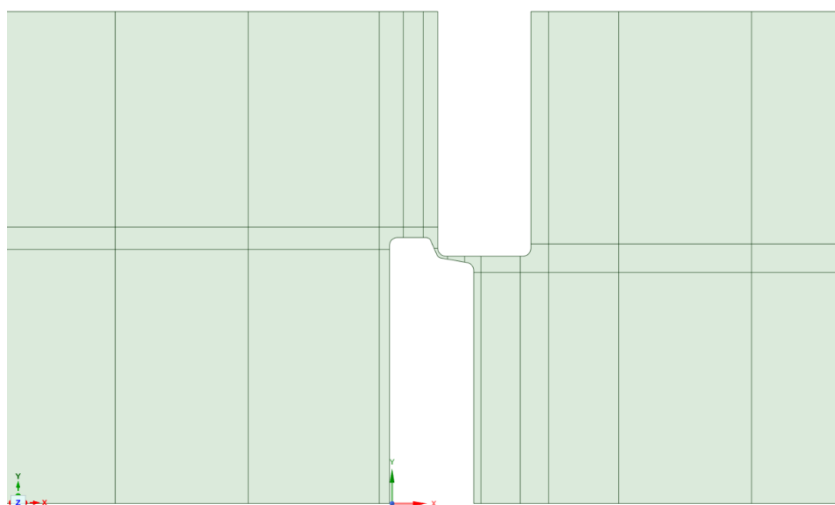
Zadaná zjednodušená 3D geometrie EGR ventilu
